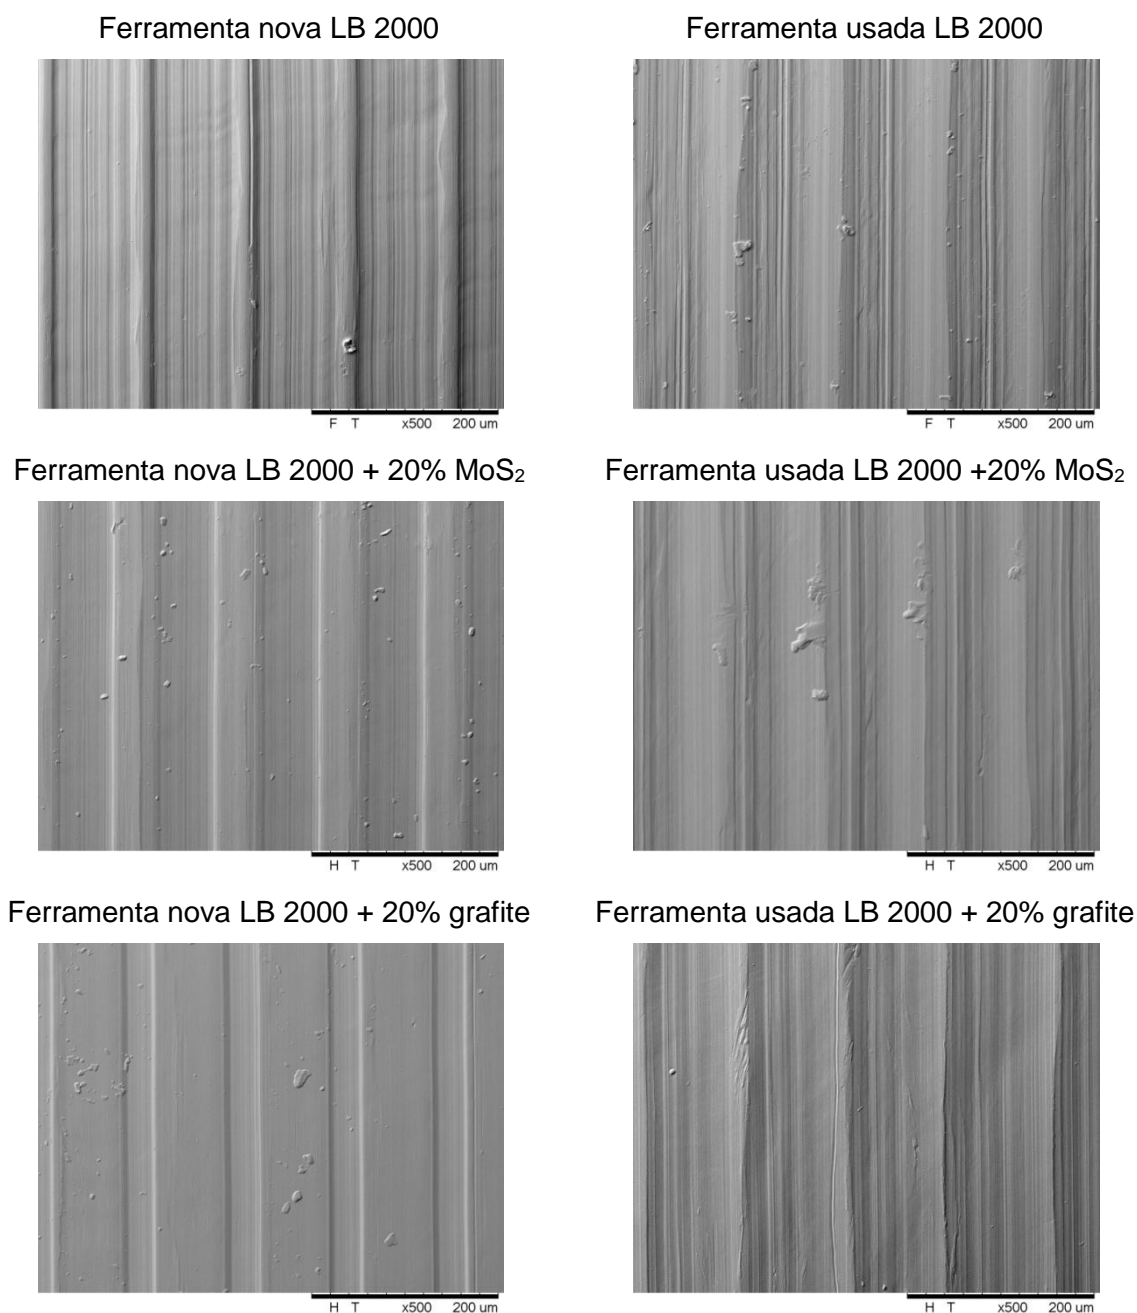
Superfícies geradas no processo de usinagem com MQF, nas diversas condições de lubri-refrigeração. Velocidade de corte 50 m/min, profundidade de corte 0,5 mm e avanço de 0,1 mm/rot
